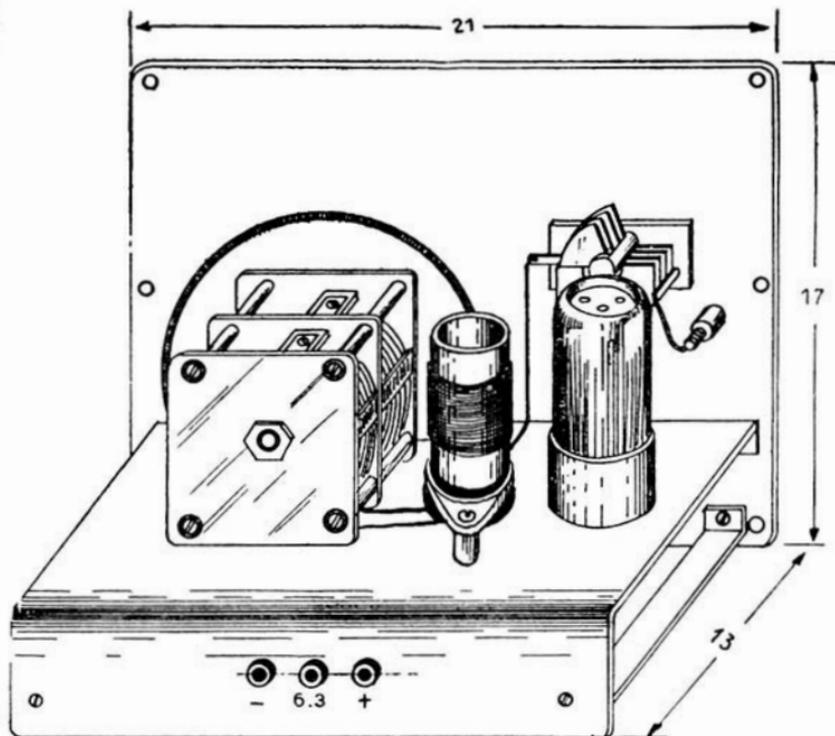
Aspetto del telaio e disposizione delle parti componenti sopra di esso.
